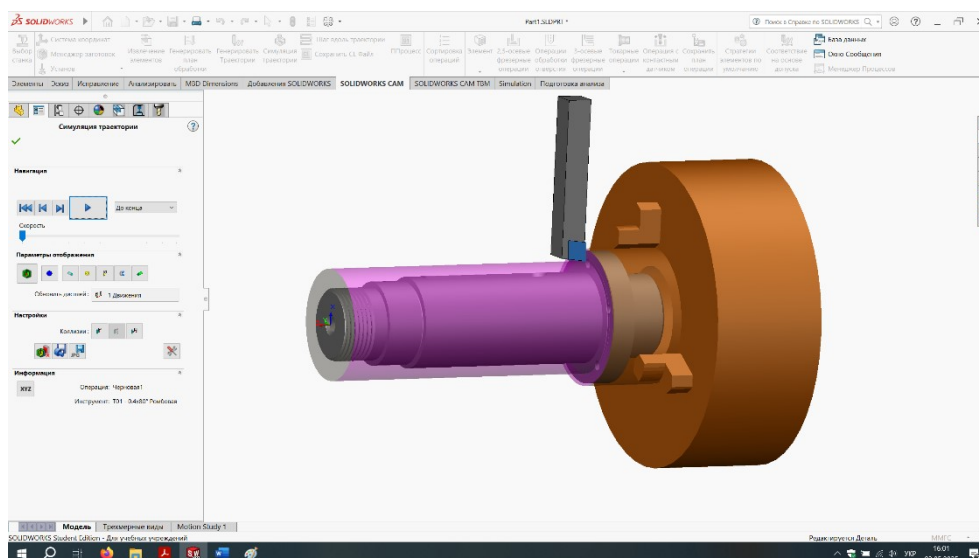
Фрагмент з чорною токарною обробкою
